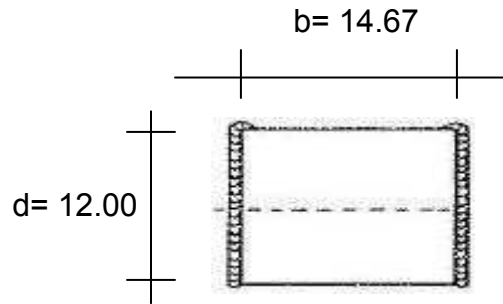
Soldadura en Bordos Laterales <sup>[13]</sup>
